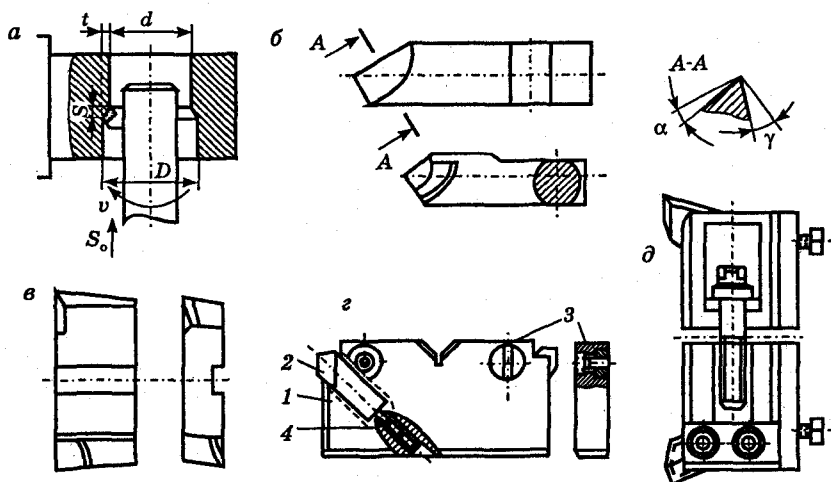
Схема и инструменты для растачивания отверстий: а — схема растачивания отверстий; б — расточные резцы; в — пластинчатые резцы; г — расточной блок; д — расточная головка
